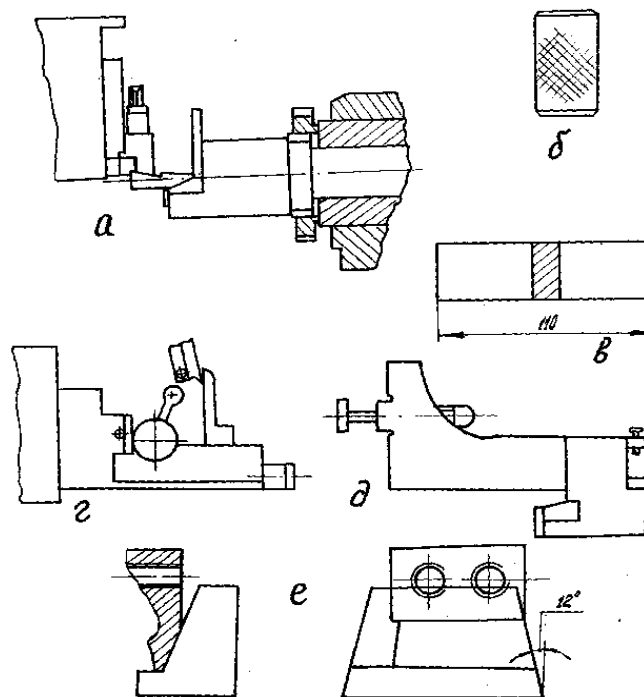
Калибры для наладки станка модели 5П23БП:
